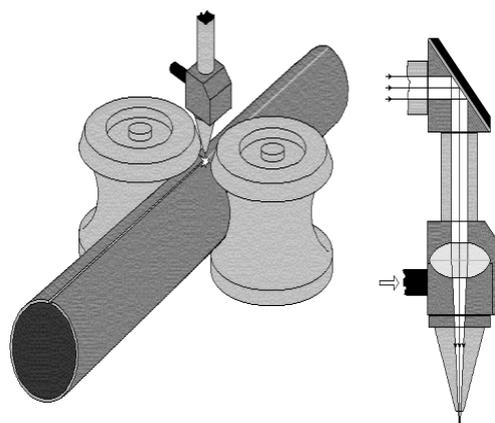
Ilustração do Processo de Soldagem por Laser. Fonte InoXTubos.
